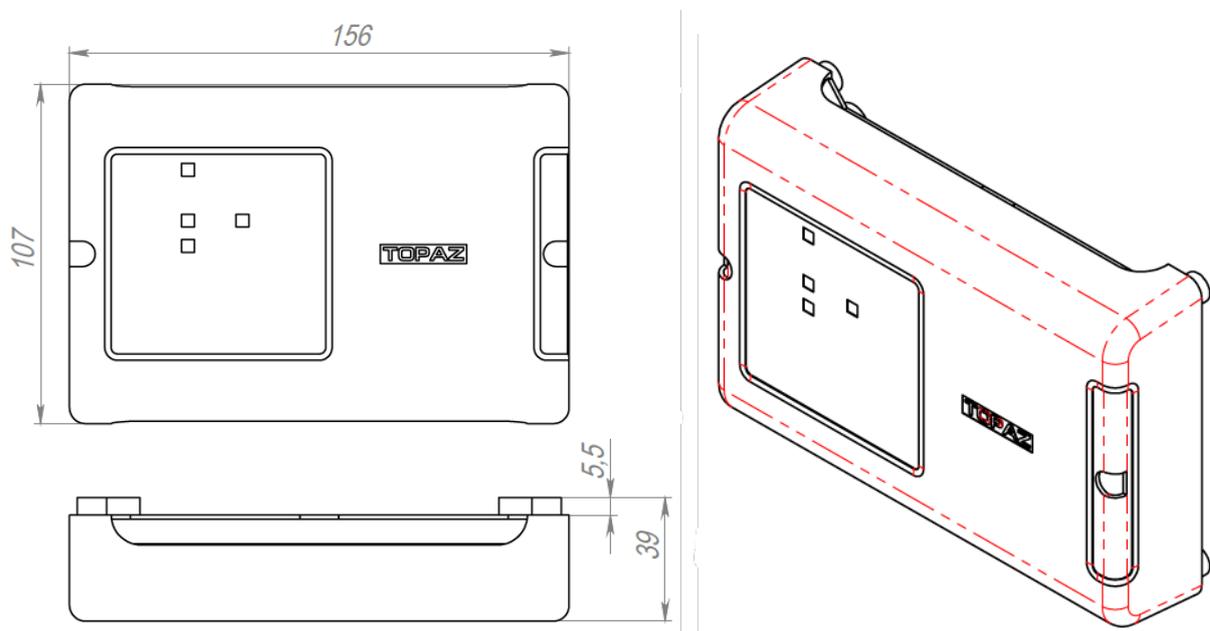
Габаритные размеры и внешний вид СП-4
